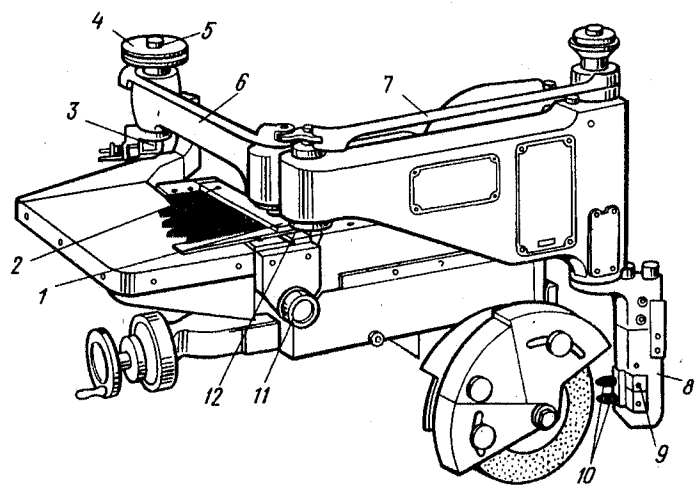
Приспособление для профильной правки кругов по копиру с пантографным механизмом
